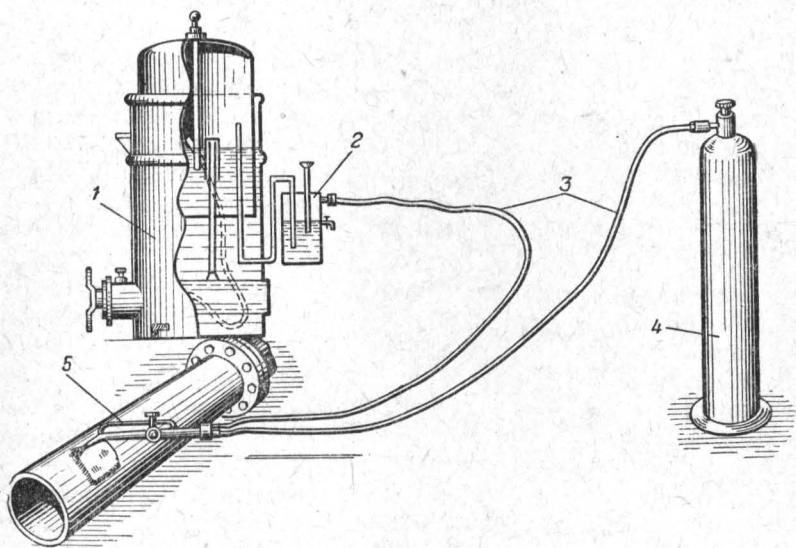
Схема установки для газовой сварки и резки металлов:
